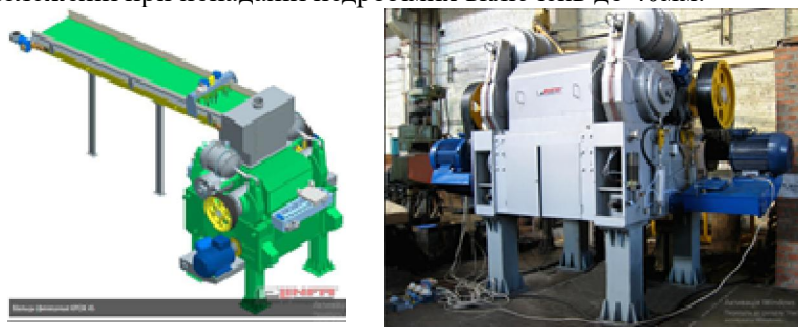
Схема і зовнішній вид валкової дробарки з фінішними вальцями КРОК 45
